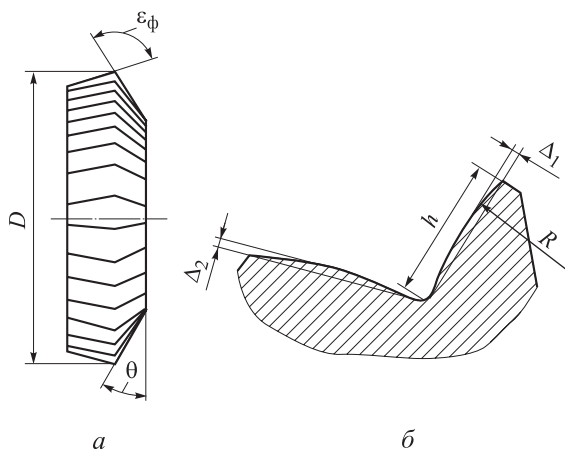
Двухугловая фреза для обработки стружечных канавок режущих инструментов (а) и профиль нормального сечения обработанной канавки (б)
